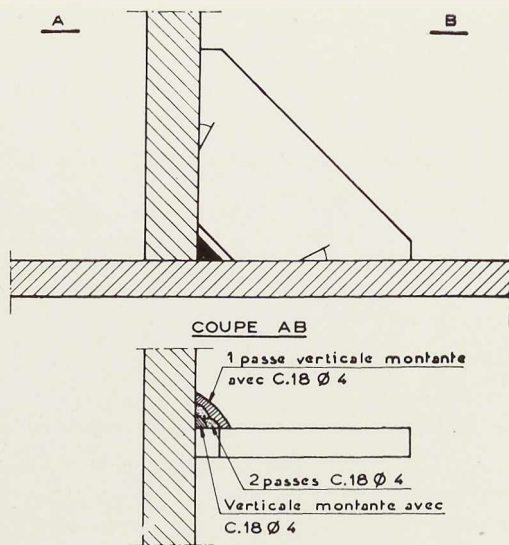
Ordre des passes pour la soudure des goussets.
